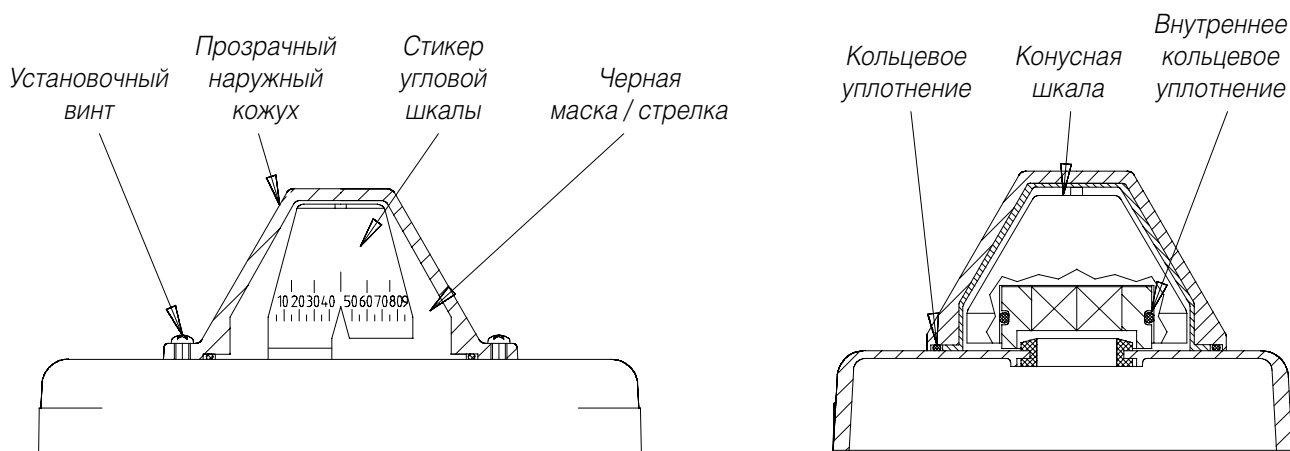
Крышка EL – Регулировка монитора Clear Cone
